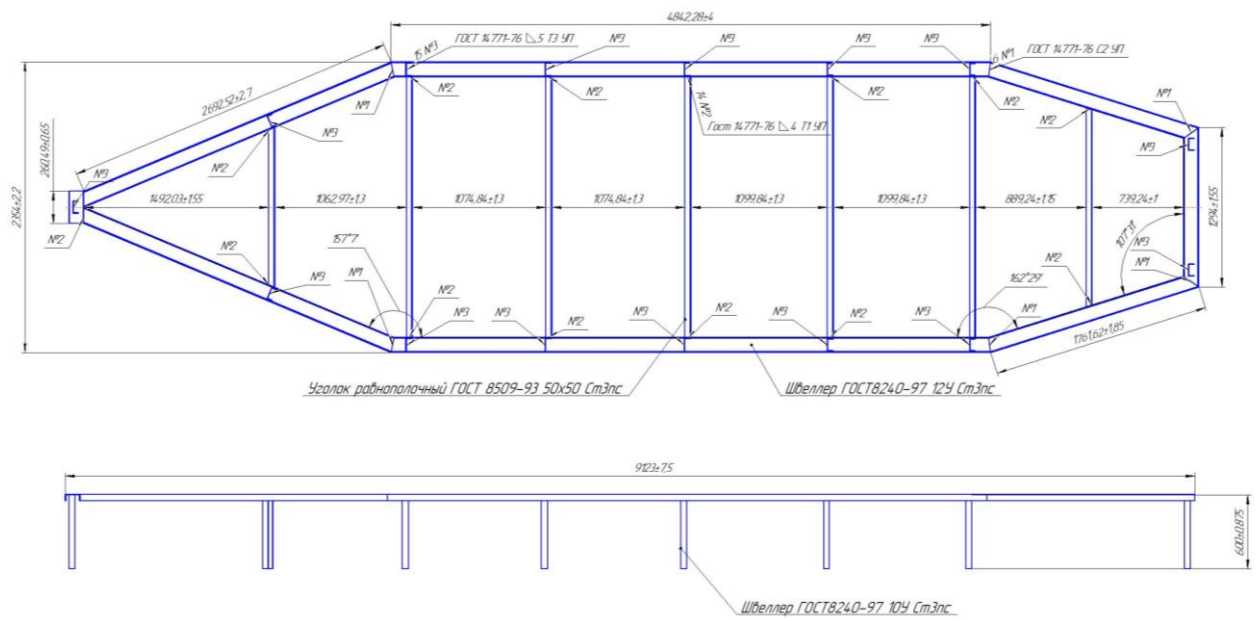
Чертёж стапеля для сборки корпуса яхты
